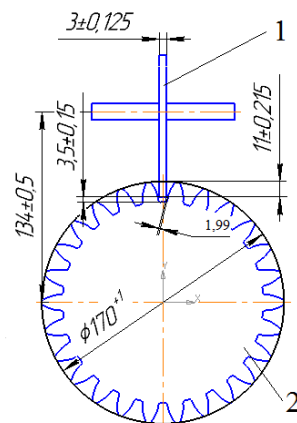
Основні установочні розміри дискового інструмента для МАО
